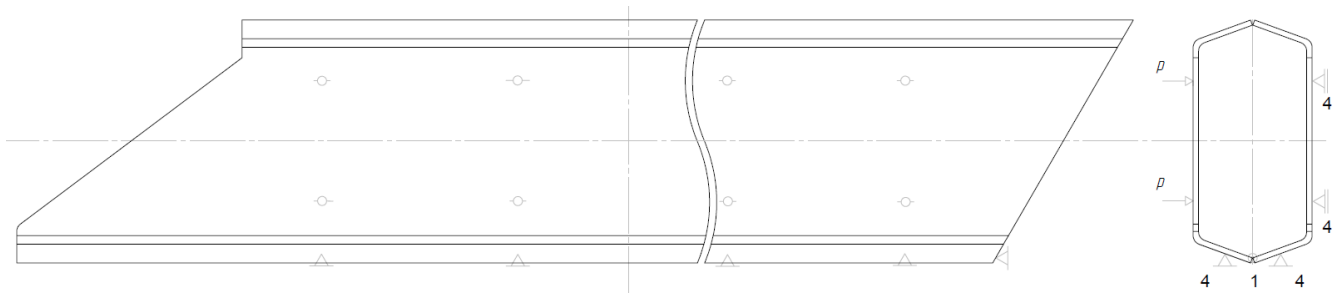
Принципиальная схема приспособления для сборки и сварки
